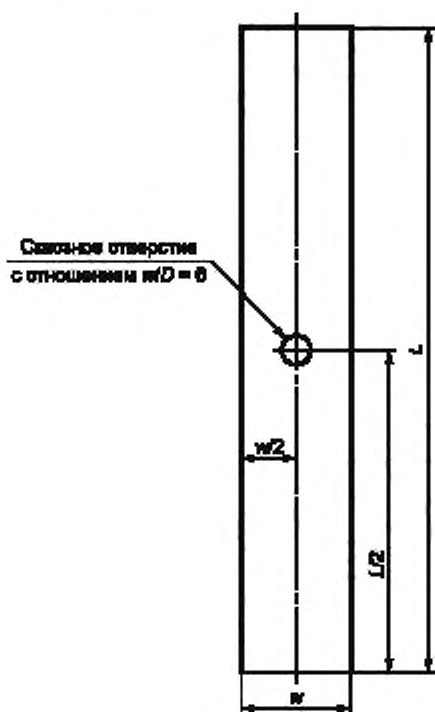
Образец ПК с открытым отверстием для испытаний на растяжение
